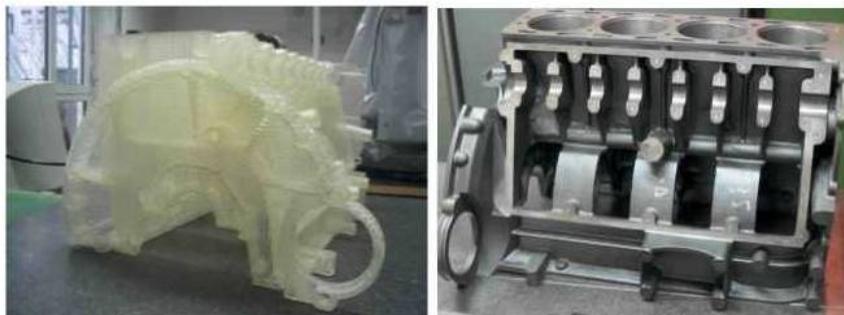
Quick-cast модель и отливка блока цилиндров
